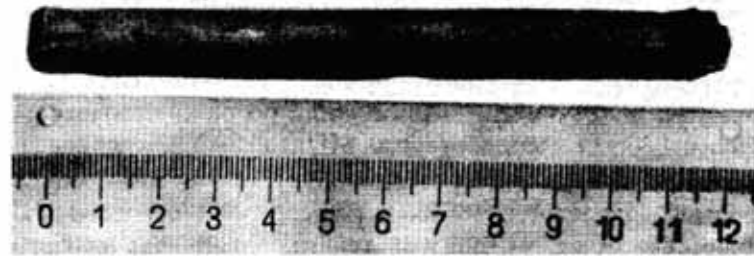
Заготовка из никелевого нанопорошка после гидростатического прессования
